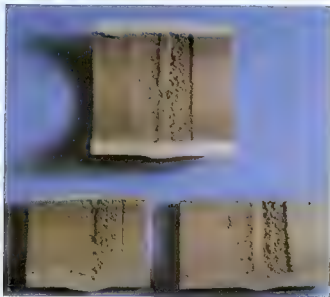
Кислотная коррозия в сварном шве
